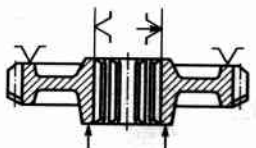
Эскиз обрабатываемого цилиндрического зубчатого колеса:
